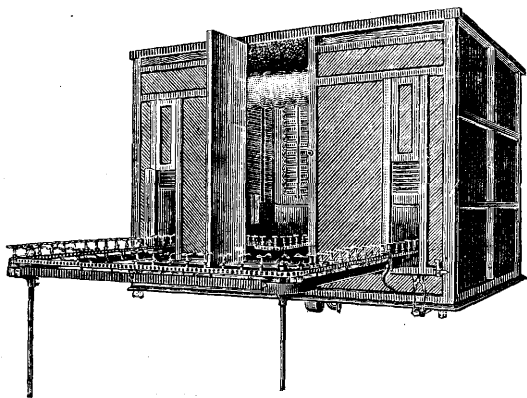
Беспрерывно действующий цепной сушильный шкаф.
